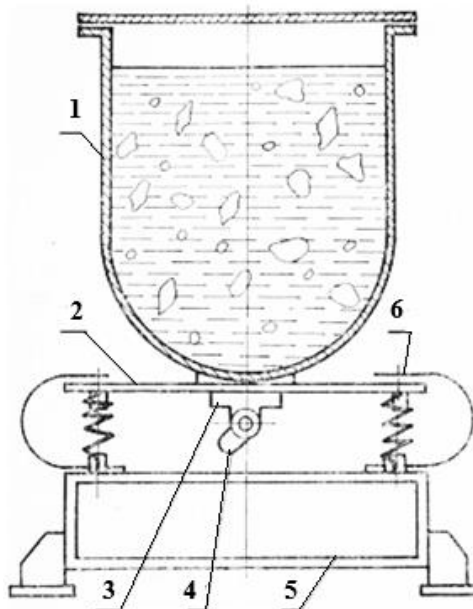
Схема установки ОМ-9312 для виброабразивной очистки:
